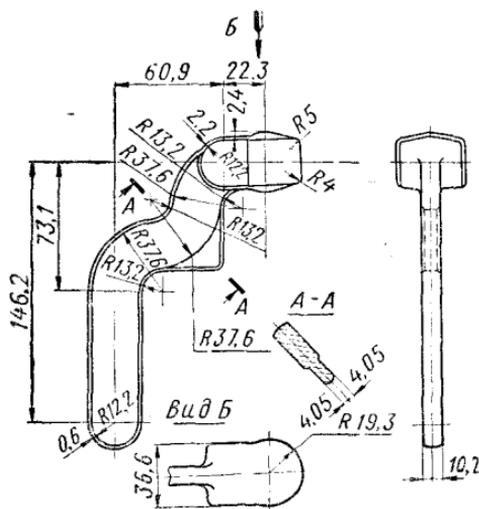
Чертеж горячей поковки рычага тормозного крана
